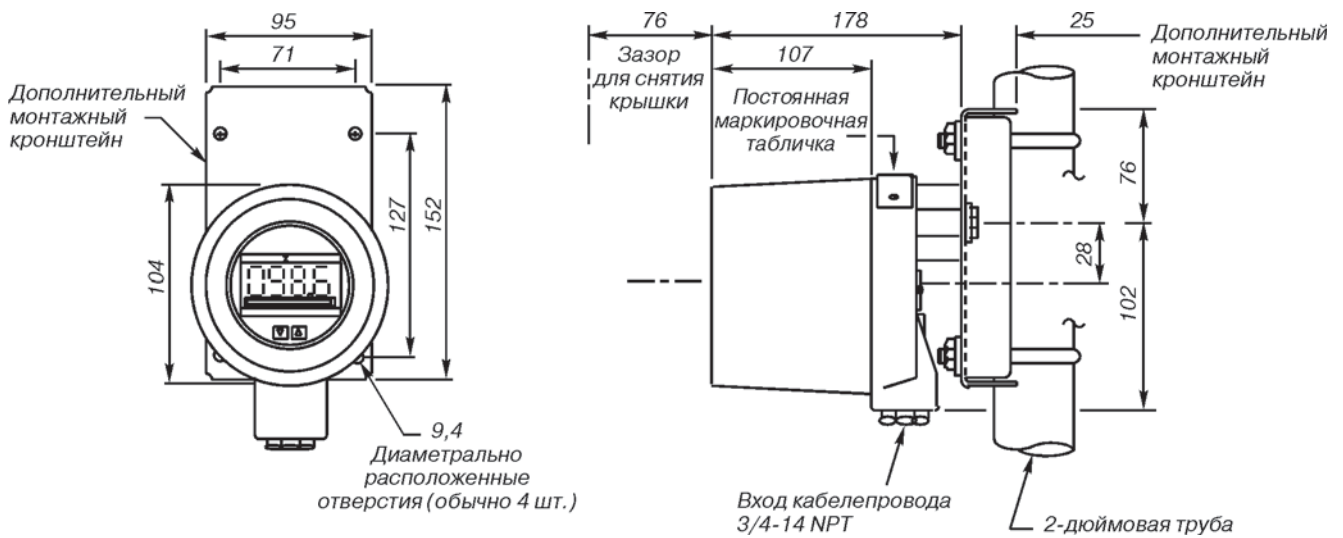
Габаритный чертеж индикатора Rosemount модели 751.
